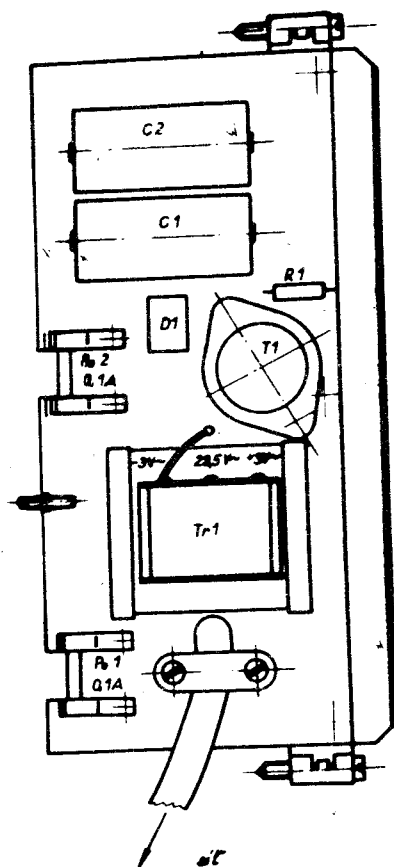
Rozmístění výstupních svorek zesilovací soupravy a umístění srážecího odporu
